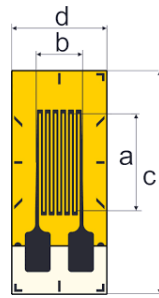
Конструкція тензорезистивної пластини. А,В,С,Д – конструкційні розміри
